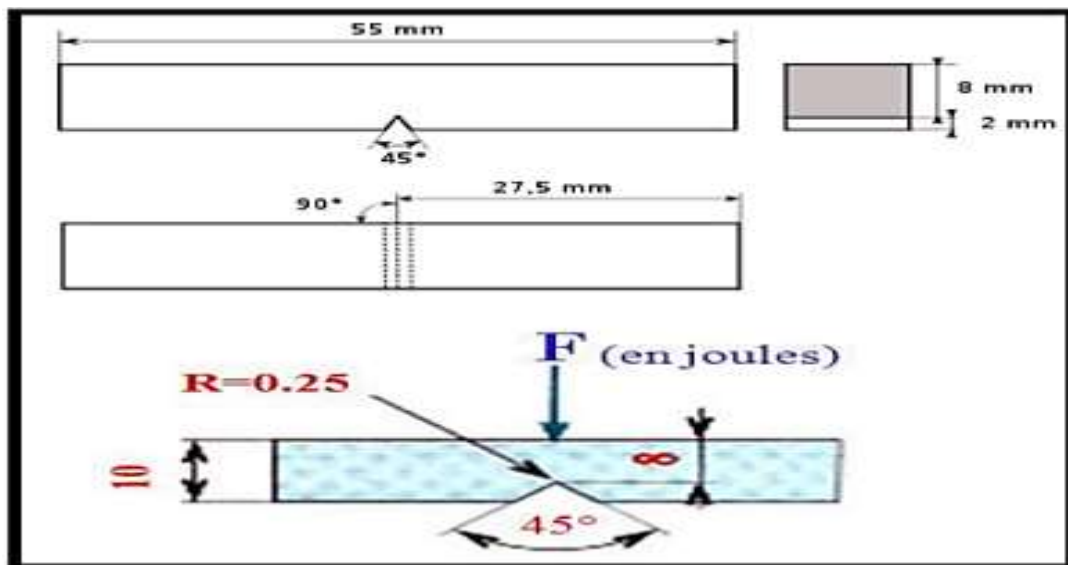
Dimensions et forme de l'éprouvette Charpy en V.
